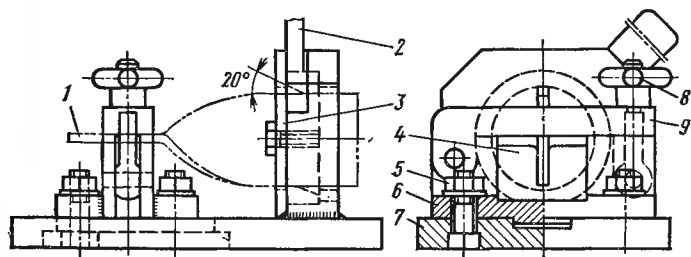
Приспособление для скручивания на 90° заготовок из медной шины:
